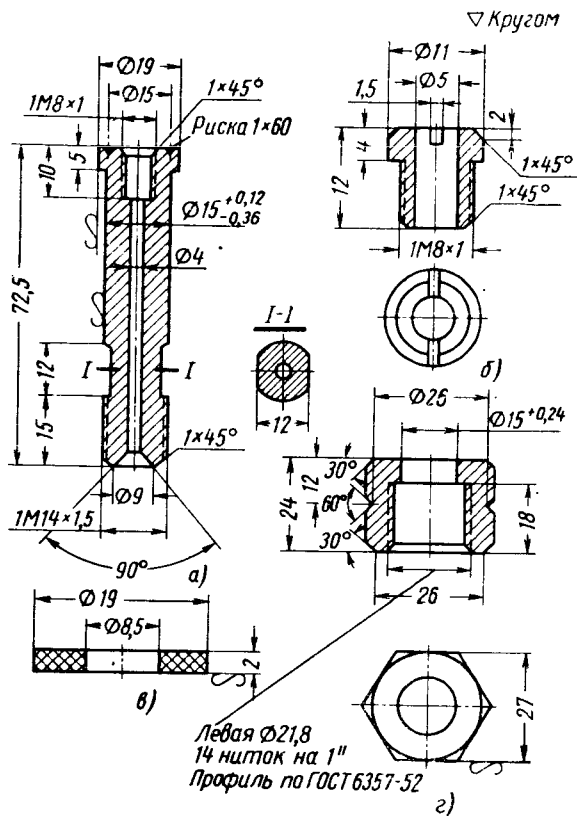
Приспособления к ацетиленовому редуктору для присоединения к баллону сжиженного газа:
